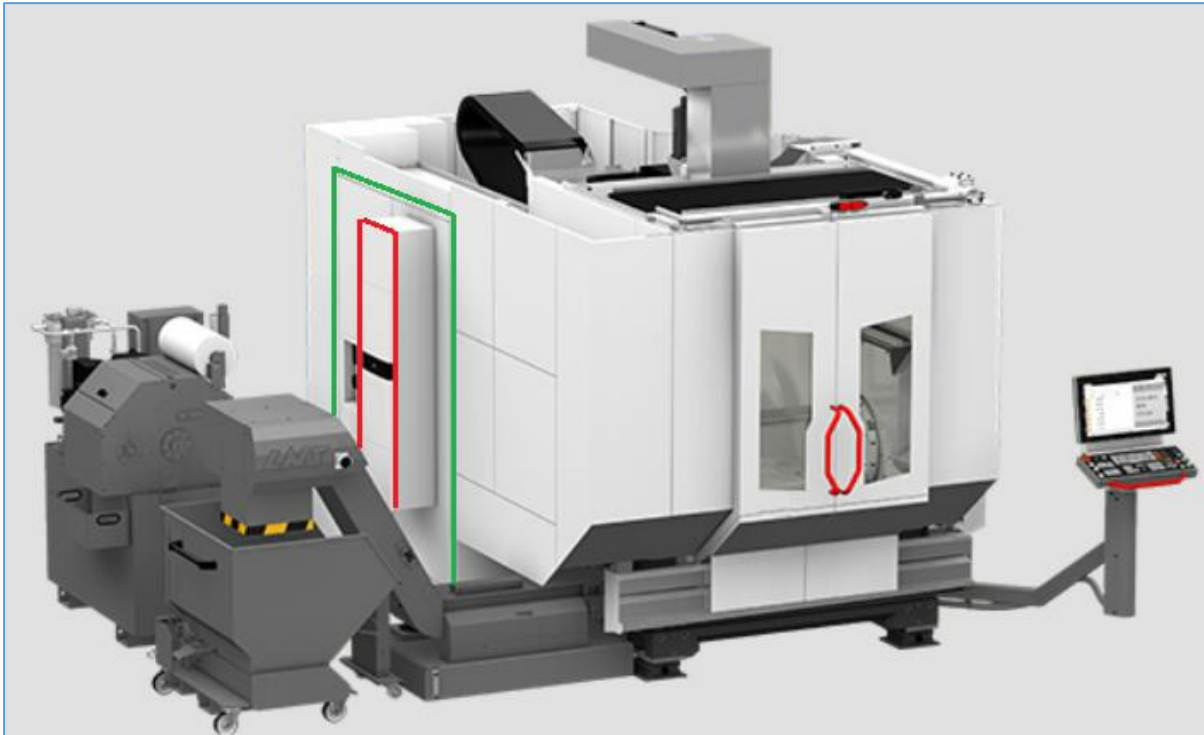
CNC-Werkzeugmaschine mit Schaltschrank (grün) und einem Klimagerät (rot) im Türanbau.
